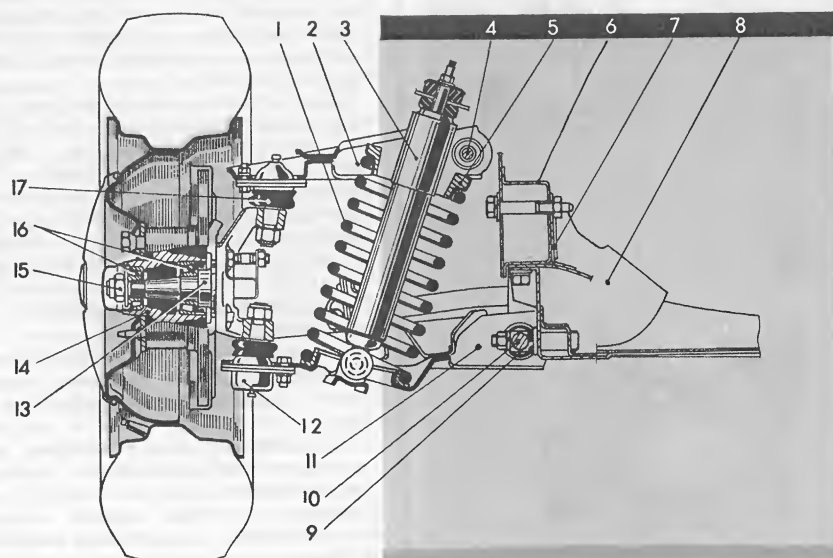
Передняя подвеска: 1 — пружина; 2 — верхний рычаг; 3 — амортизатор; 4 — ось верхнего рычага; 5 — резиновая прокладка; 6 — лонжерон кузова; 7 — регулировочная пластина; 8 — поперечина подвески; 9 — пакет шайб; 10 — ось нижнего рычага; 11 — нижний рычаг; 12 — нижний шаровой шарнир; 13 — стойка; 14 — ступица; 15 — гайка ступицы; 16 — подшипники; 17 — верхний шаровой шарнир.
